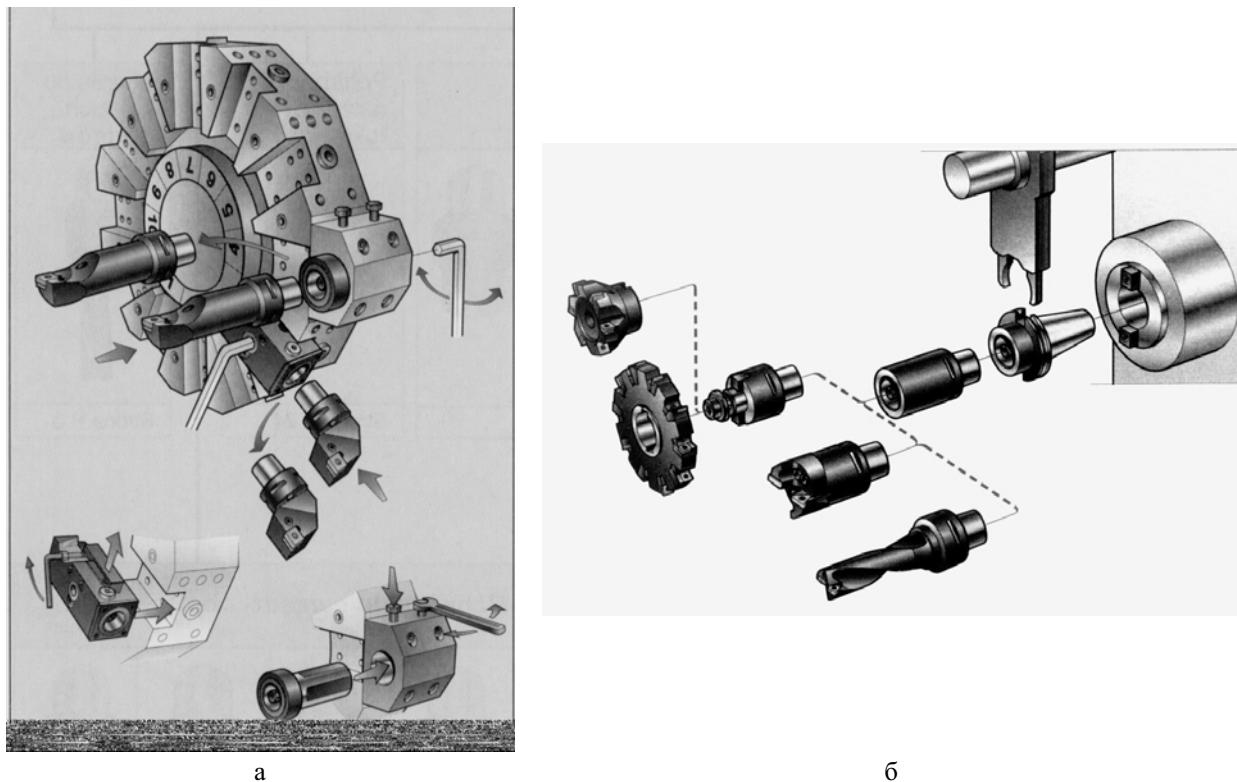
Модульна інструментальна система Coromant Capto фірми Sandvik для ручного закріплення інструментів у револьверній головці токарного верстата (а) та в револьверній головці з малою кількістю гнізд токарно-фрезерного верстата з ЧПК (б)
